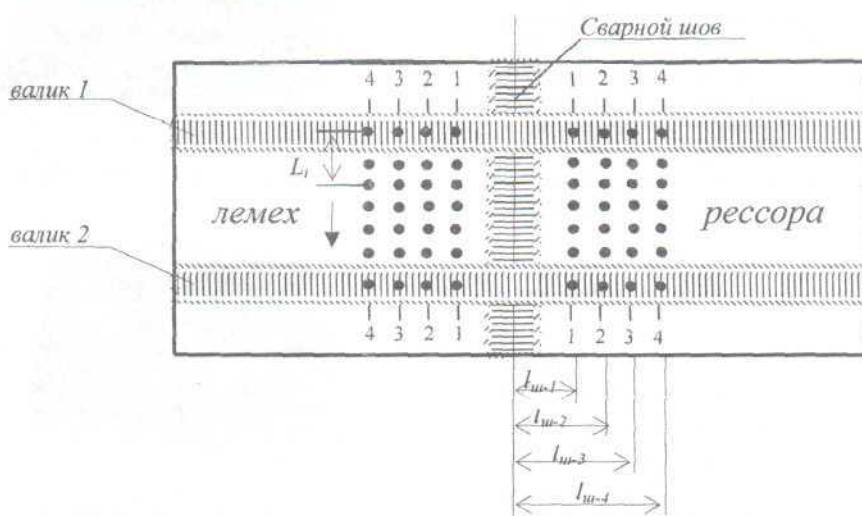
Схема измерения твердости сварного шва, армирующих валиков и околошовных областей на образце №4
